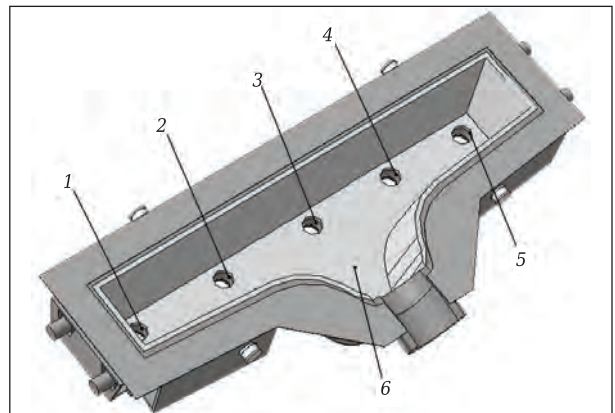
Компоновка промежуточного ковша: 1–5 — разливочные отверстия ковша; 6 — бойное место
